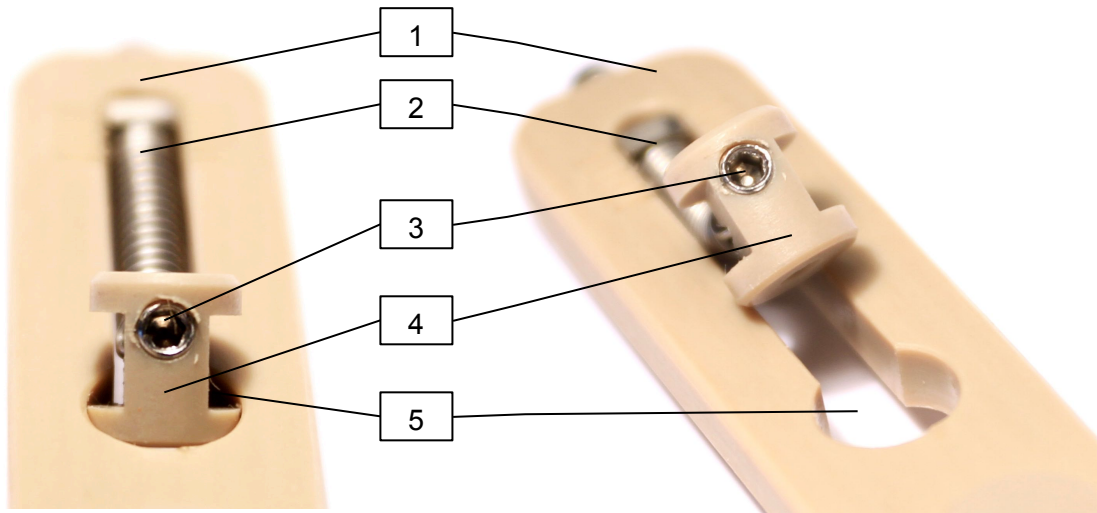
Aufsicht auf den Gleitschlitten mit Ausschnitten für die Rahmenschiene. 1) distaler Distraktorschenkel 2) Feder mit Federjustierschraube 3) Madenschraube zur K-Draht Fixierung 4) Federschlitten 5) Ausschnitt für Federschlitten
